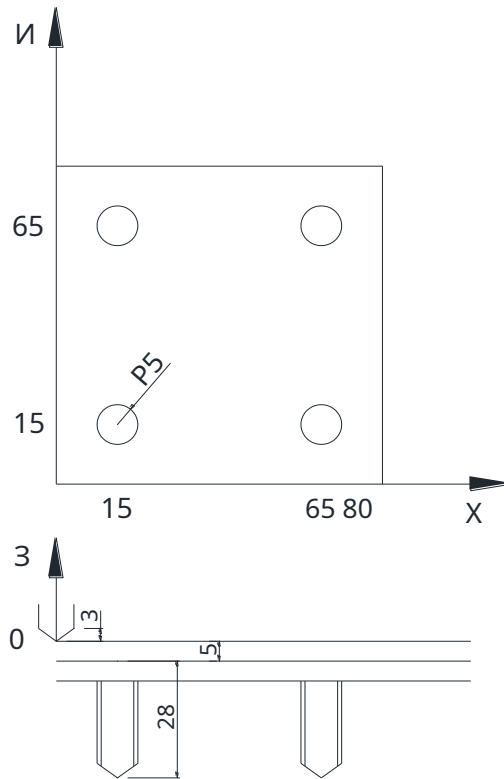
Эскиз 4 процесса обработки заготовки
